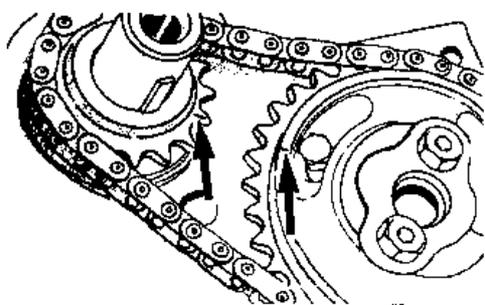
А.14. Установочные метки звездочек цепи привода распределительного вала
